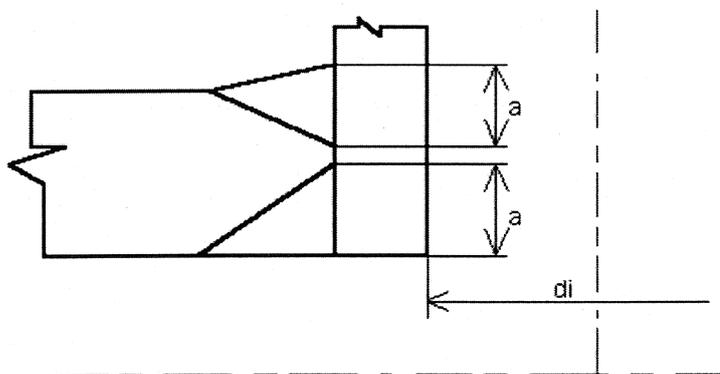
Definition von „a“ für die Schweißnahtarten 17, 18 und 19
